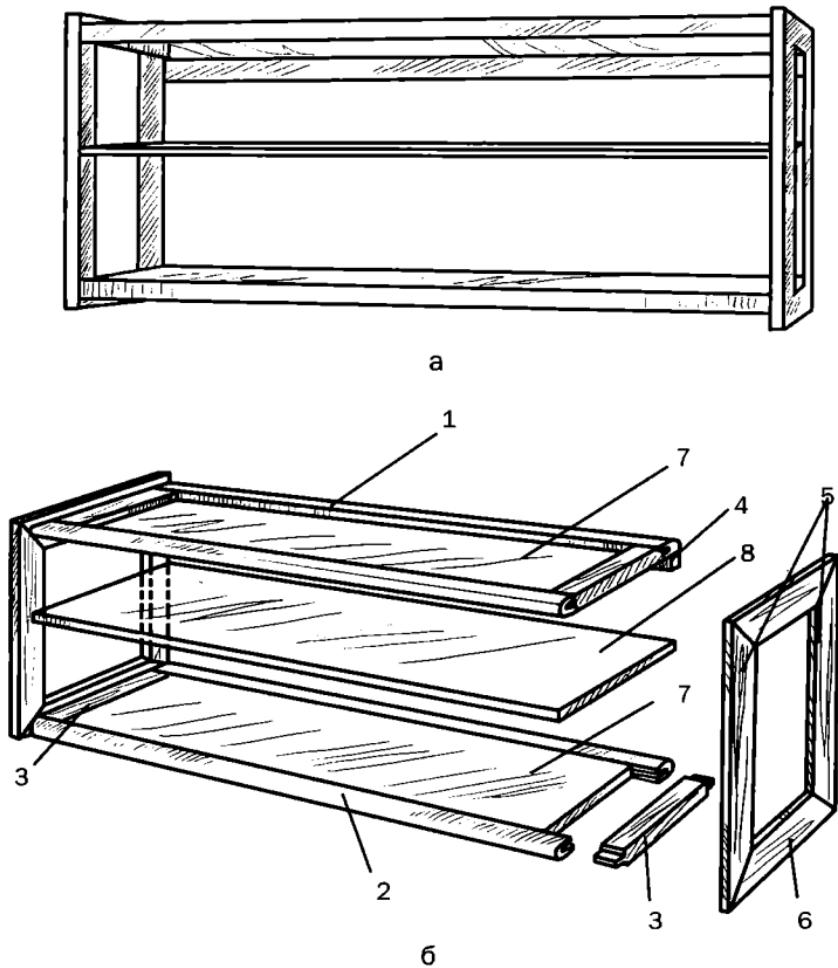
Полка из армированного стекла: а — общий вид; б — схема сборки: 1, 2 — продольные бруски; 3 — поперечные бруски; 4 — крепежный брусок; 5, 6 — бруски боковин; 7, 8 — стекло
